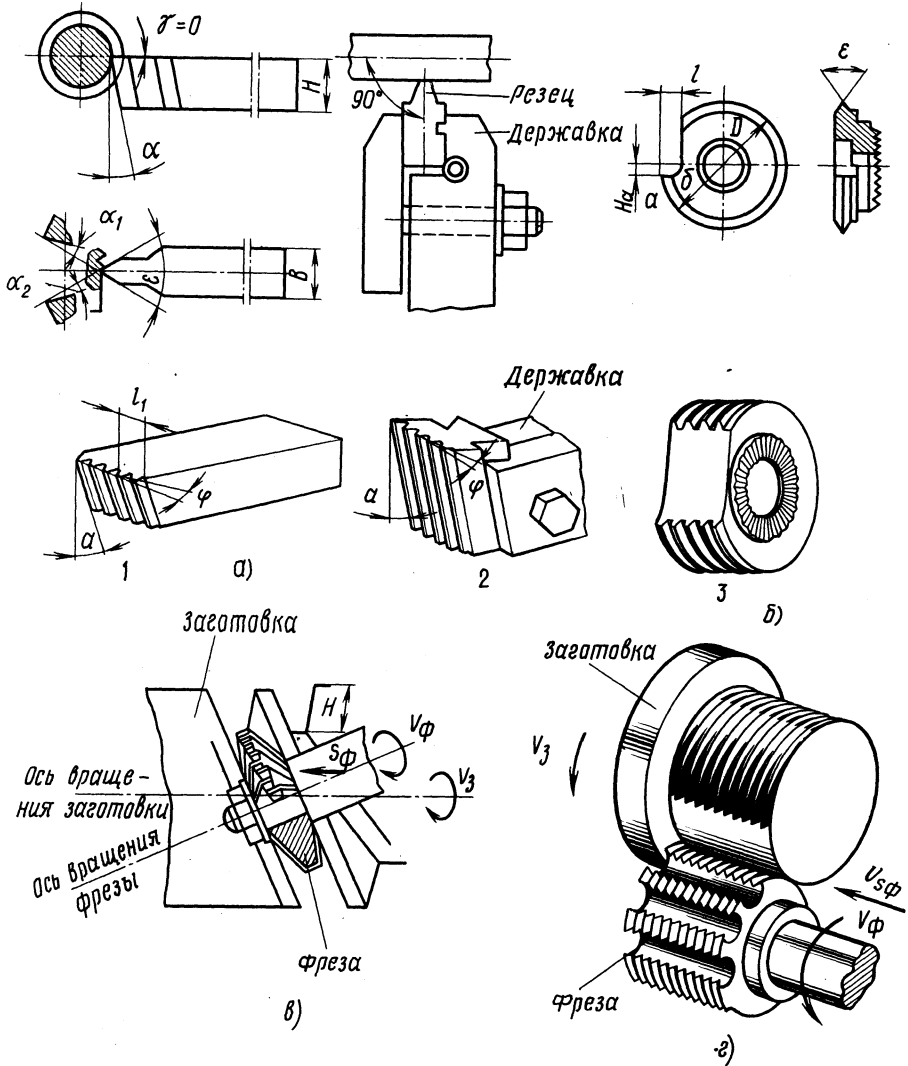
Схемы нарезания резьбового профиля призматическим (а) и дисковым (б) резцом, обычными (в) и дисковыми (г) фрезами
